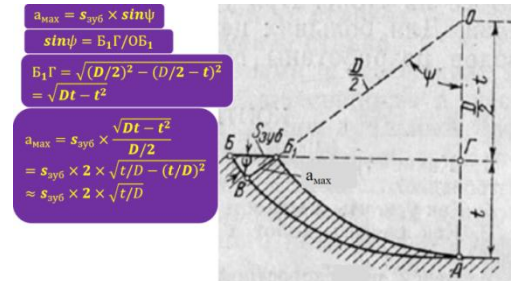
Сечение срезаемого слоя при попутном фрезеровании цилиндрической или концевой фрезой
